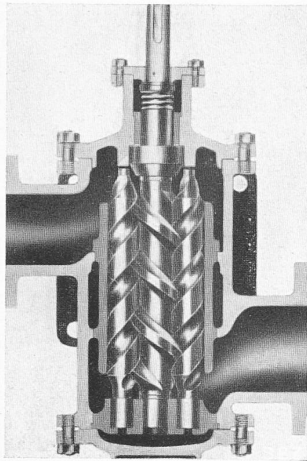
Schraubenpumpe mit stufenweiser Fördermenge
